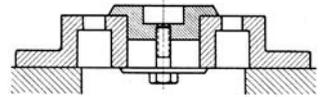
Einlage für einen innen vorgearbeiteten Zuschnitt.
